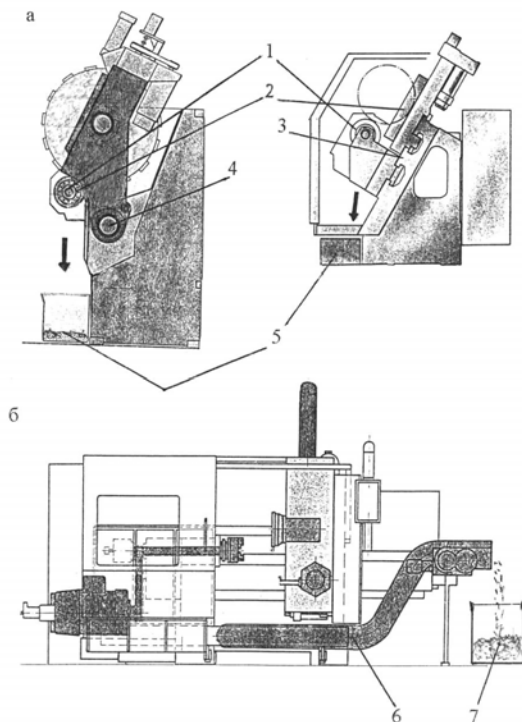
Схема автоматизации уборки стружки на токарных станках с ЧПУ: а – свободный сход стружки; б – компоновка транспортера для удаления стружки; 1 – шпиндель; 2 – каретка с инструментом; 3 – плоские направляющие; 4 – круглые направляющие; 5 – место сбора стружки; 6 – транспортер; 7 – приемное устройство для стружки
